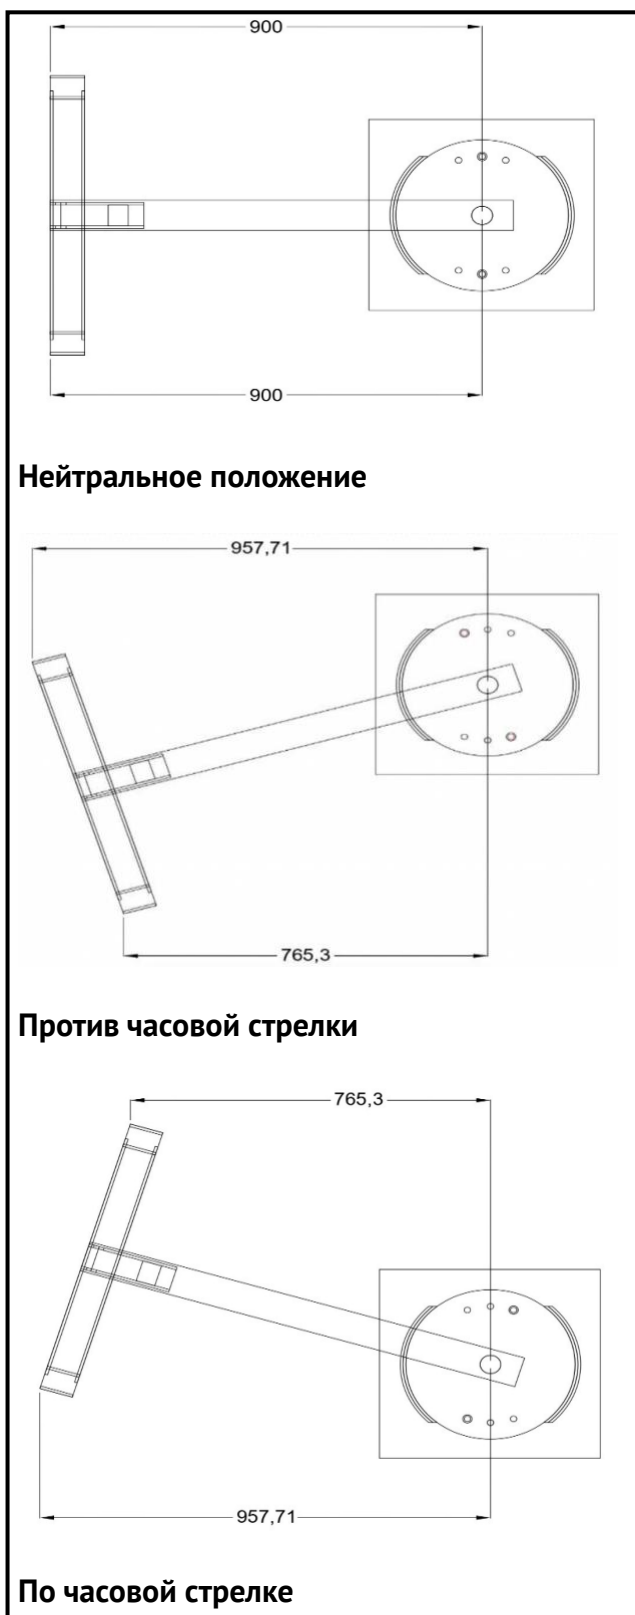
Положения поворотного механизма навески: нейтральное, против часовой стрелки, по часовой стрелке
